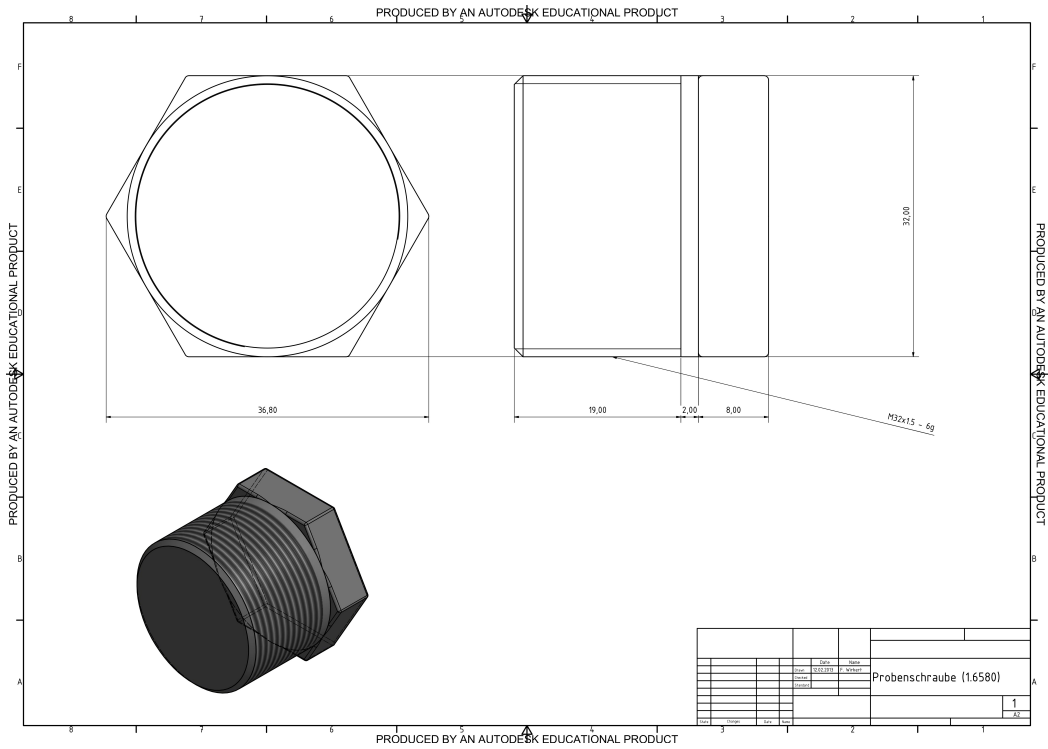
Technische Zeichnung Proben-Stempel-Schraube
